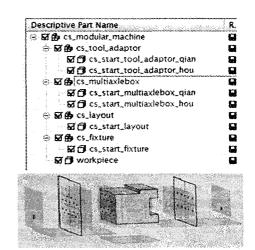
孔加工组合机床结构装配树及对应总体控制结构 Fig. 4 Hole machining combination machine structure assembly tree corresponds to the overall control structure
